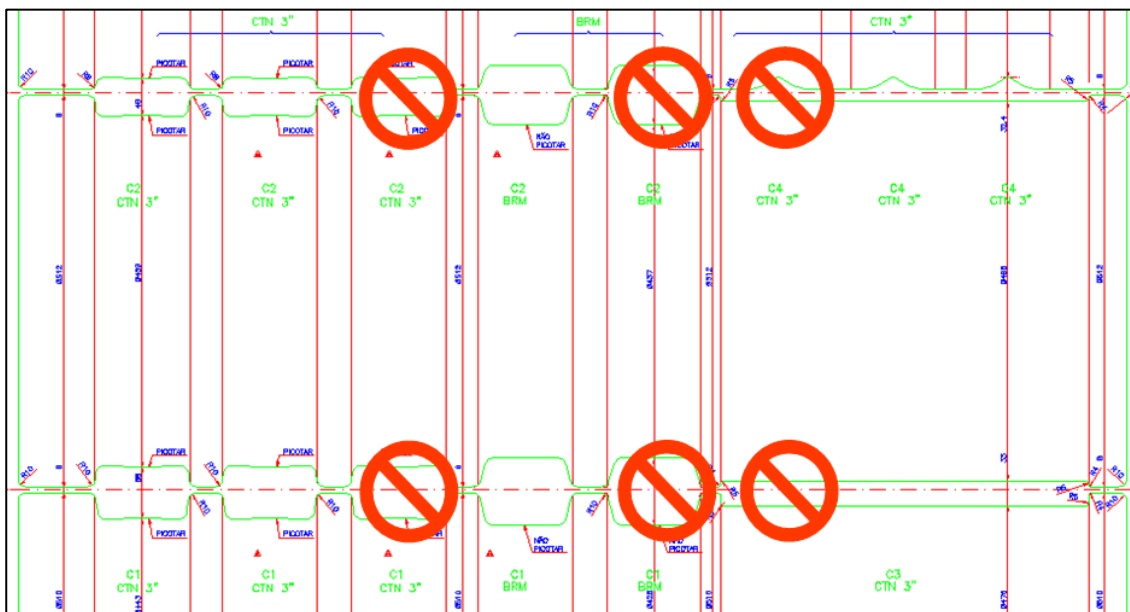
Proposta de alteração do plano de passes da cadeira 1.
